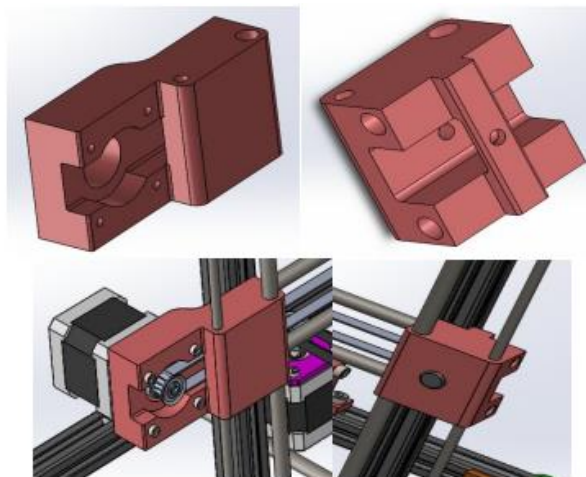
Porte moteur horizontal et porte pignon horizontal
